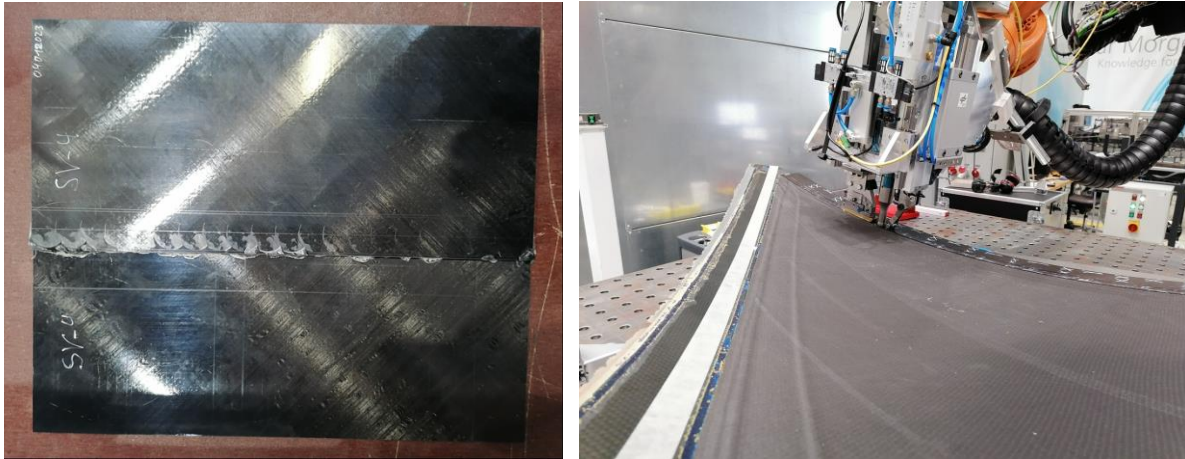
Ultraschallschweißversuche im MultiSpot-Verfahren (links) und an gekrümmten Strukturen (rechts)
